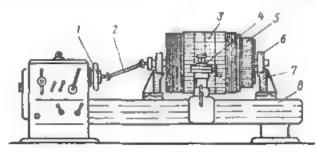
Якорь, установленный для проточки коллектора на токарно-ванторезном станке
